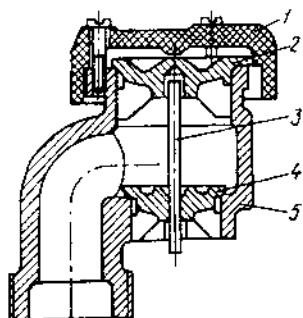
Поворотные устройства (трубы) резервуаров:
